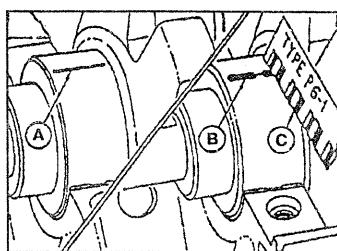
Измерение зазора в подшипнике (A - пластмассовая нить; B - распластанная нить; C - шкала).
